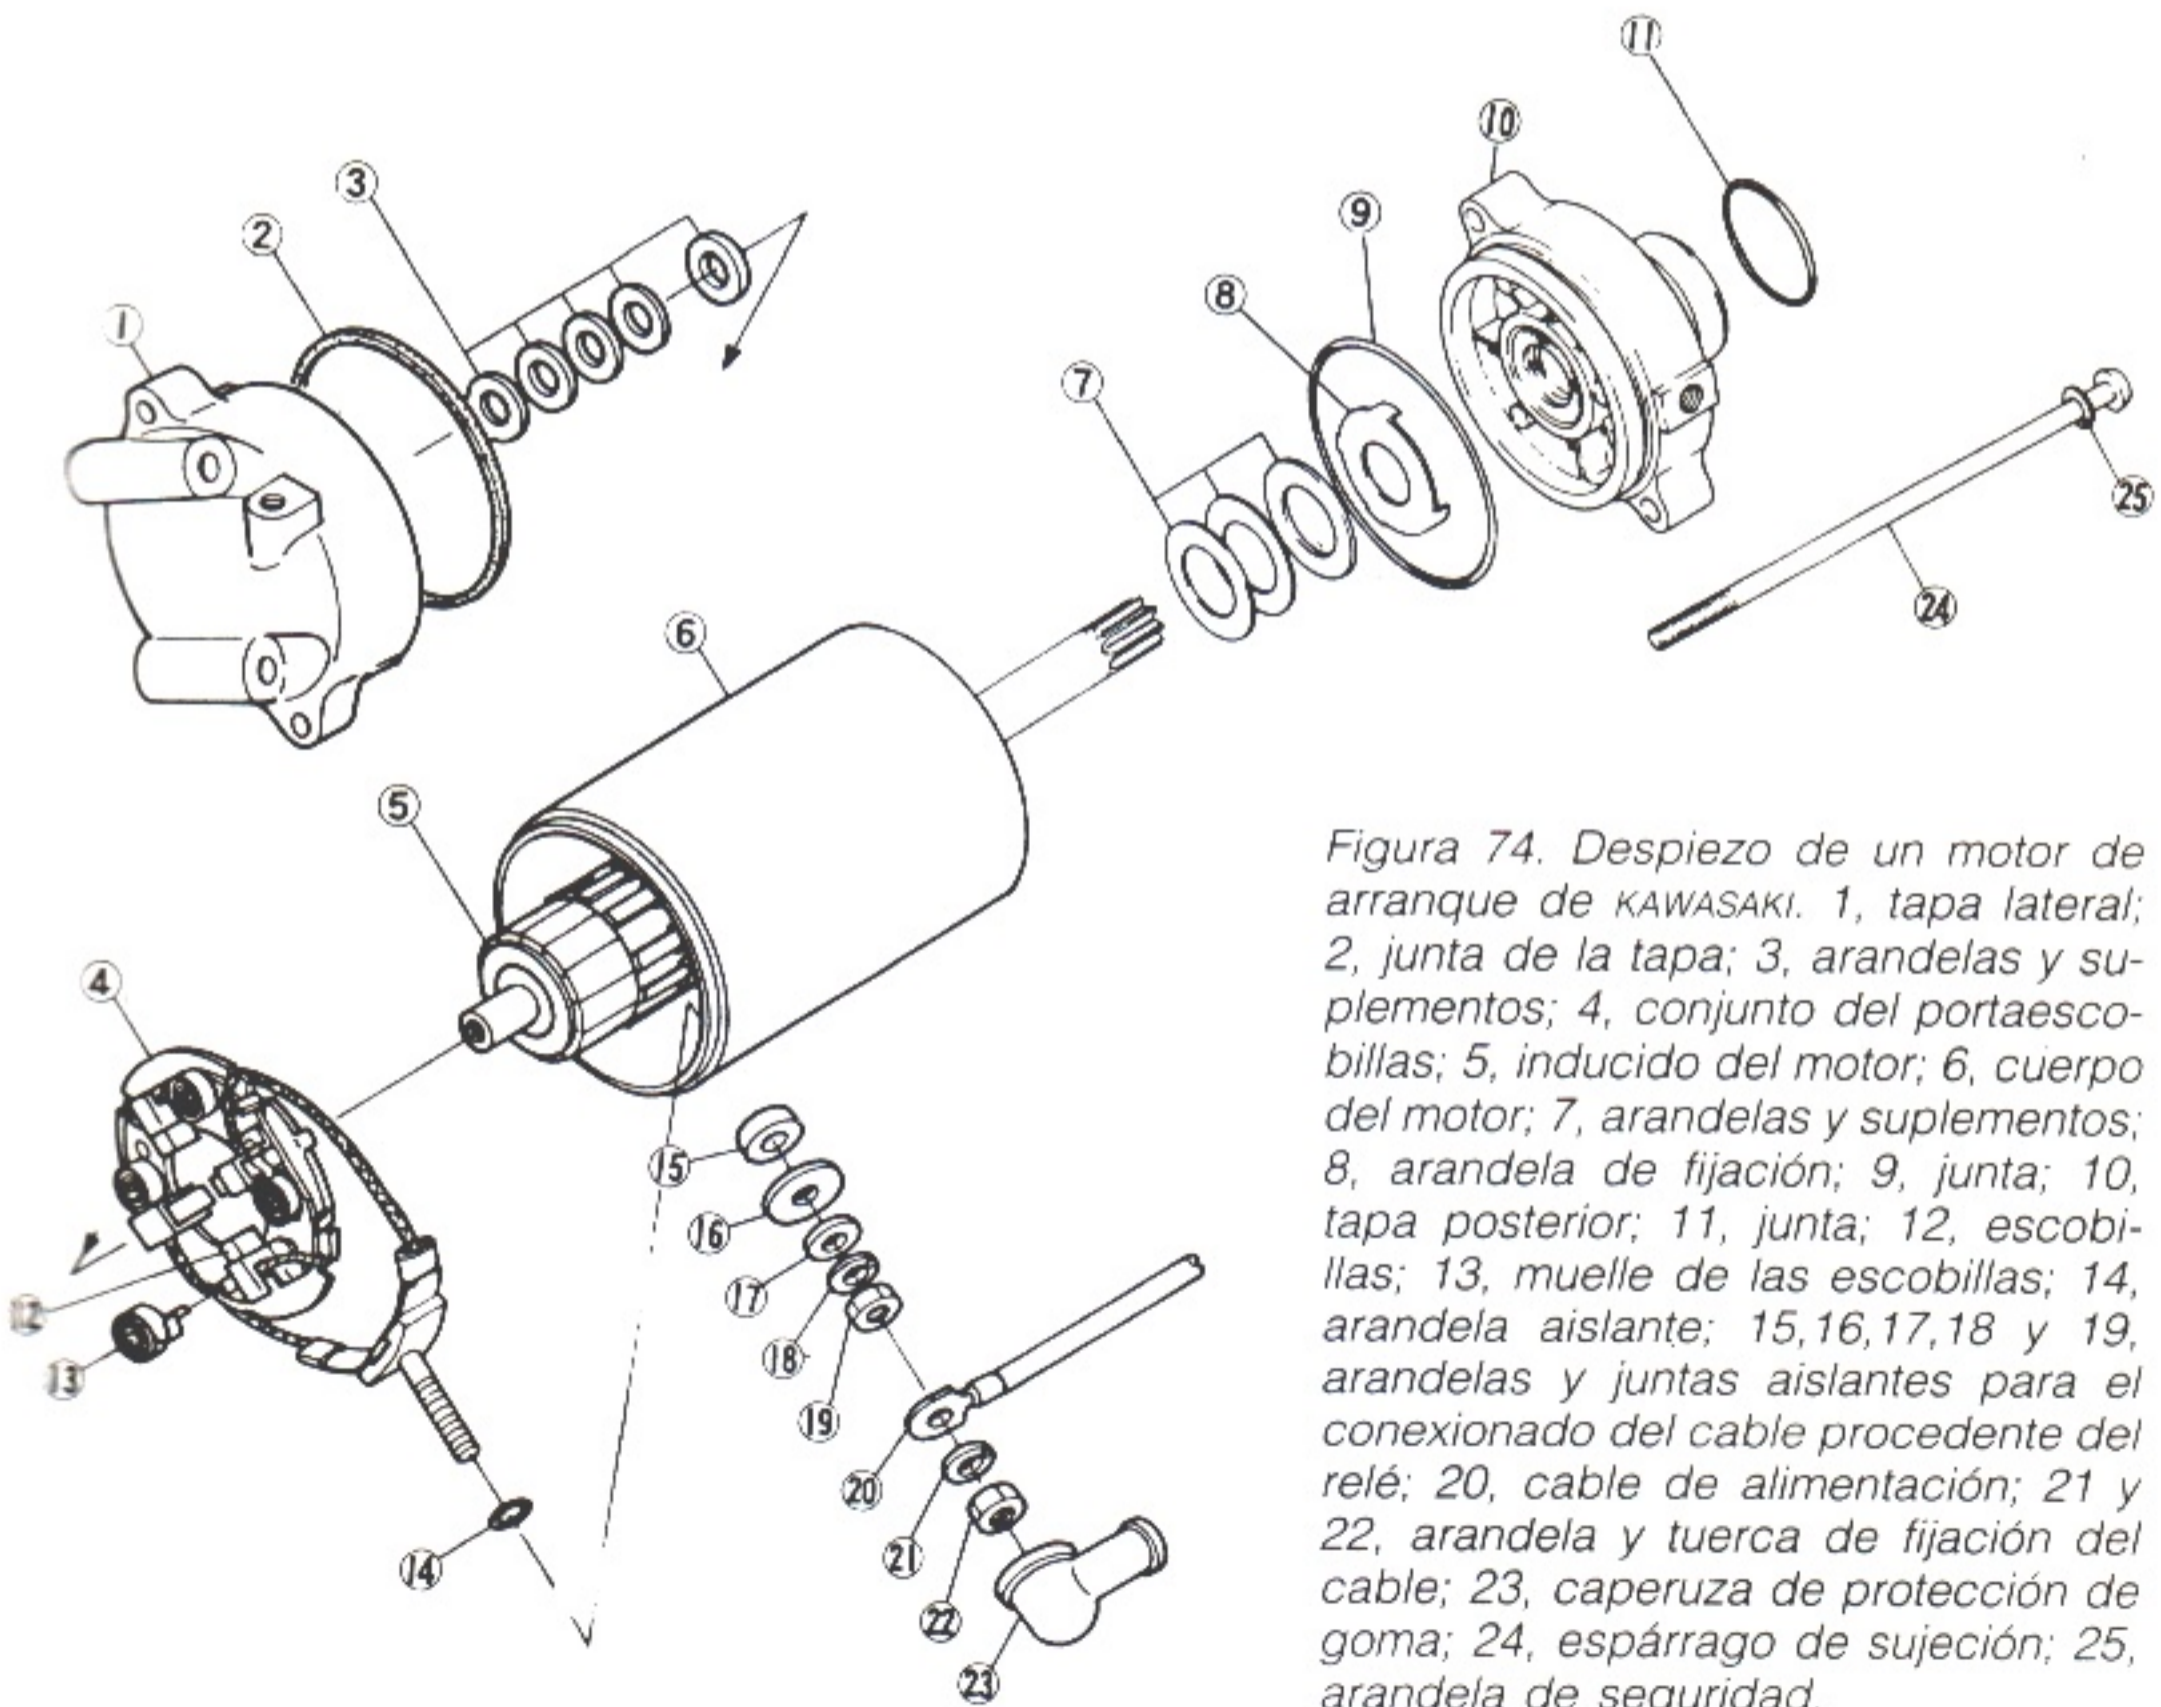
Despiece de un motor de arranque de KAWASAKI. 1, tapa lateral; 2, junta de la tapa; 3, arandelas y suplementos; 4, conjunto del portaescobillas; 5, inducido del motor; 6, cuerpo del motor; 7, arandelas y suplementos; 8, arandela de fijación; 9, junta; 10, tapa posterior; 11, junta; 12, escobillas; 13, muelle de las escobillas; 14, arandela aislante; 15, 16, 17, 18 y 19, arandelas y juntas aislantes para el conexionado del cable procedente del relé; 20, cable de alimentación; 21 y 22, arandela y tuerca de fijación del cable; 23, caperuza de protección de goma; 24, espárrago de sujeción; 25, arandela de seguridad.
